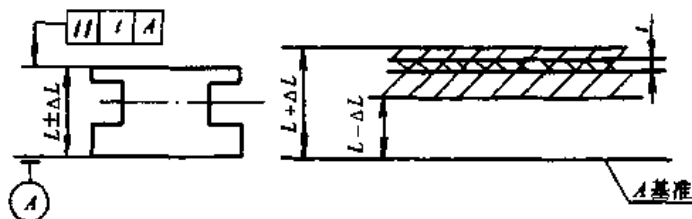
形位公差带在尺寸公差带内浮动
